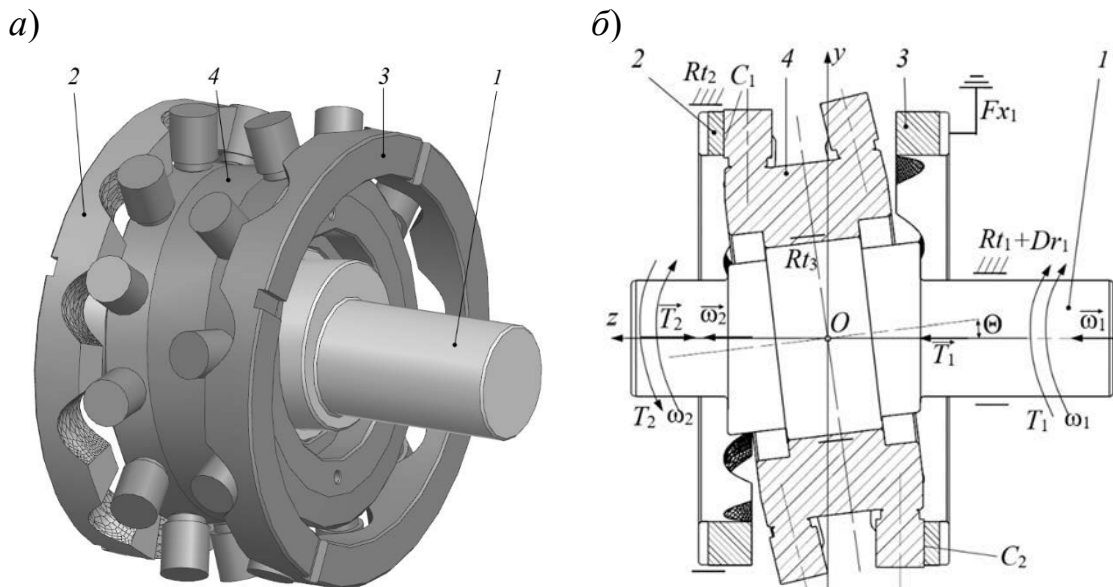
Модель СРП с двухрядным сателлитом: а – общий вид; б – с обозначением шарниров, контактов и нагрузок
